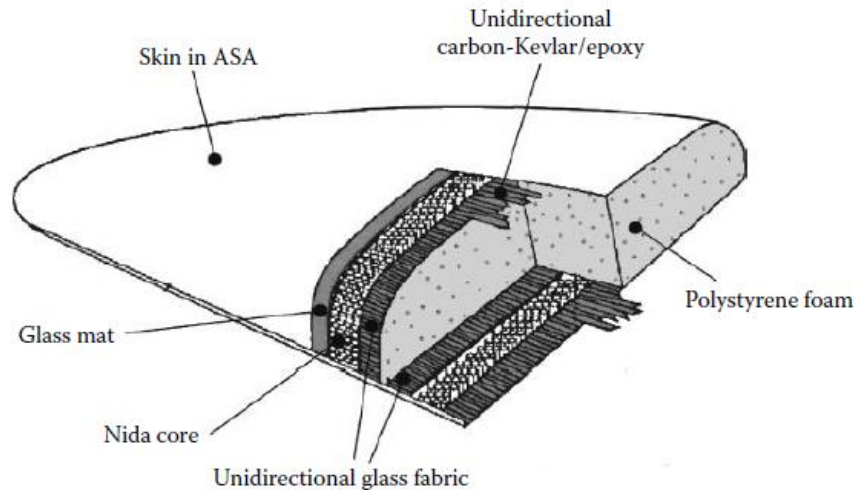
Prancha de surf em estrutura *sandwich* [3]
